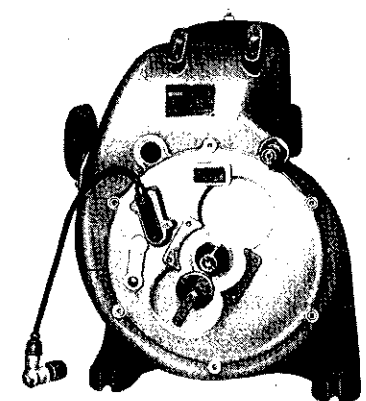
Gehäusedeckel mittels zweier Schraubenzieher abdrücken
